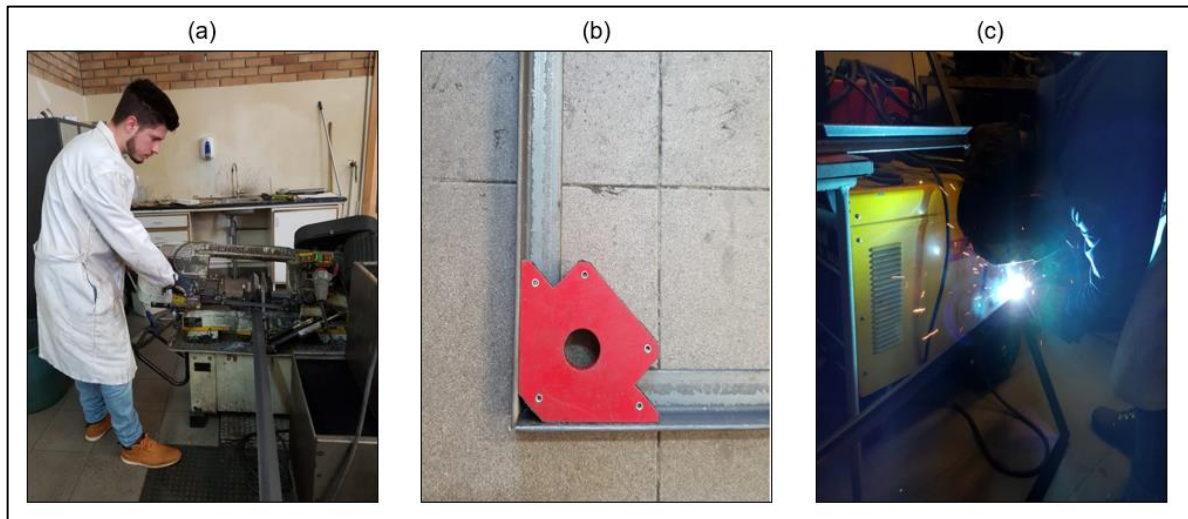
Etapas do processo de fabricação do sistema; (a) corte das cantoneiras, (b) alinhamento e (c) soldadura.
